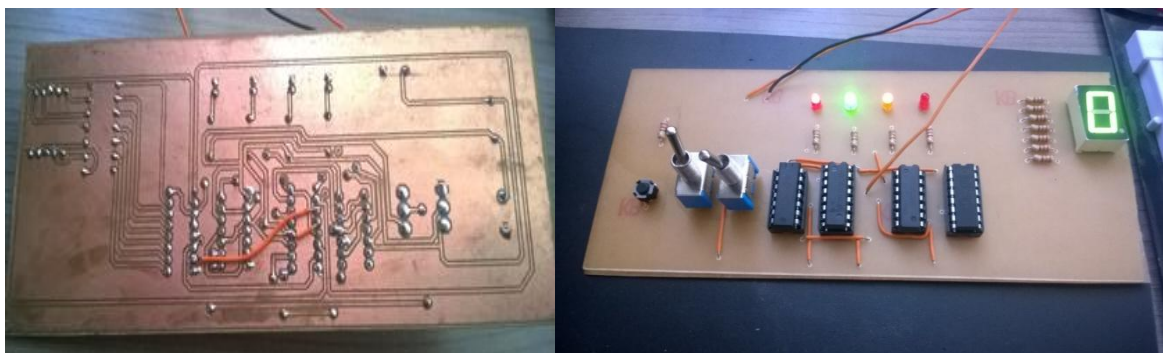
Placa de circuito impresso para uso no tanque de corrosão
